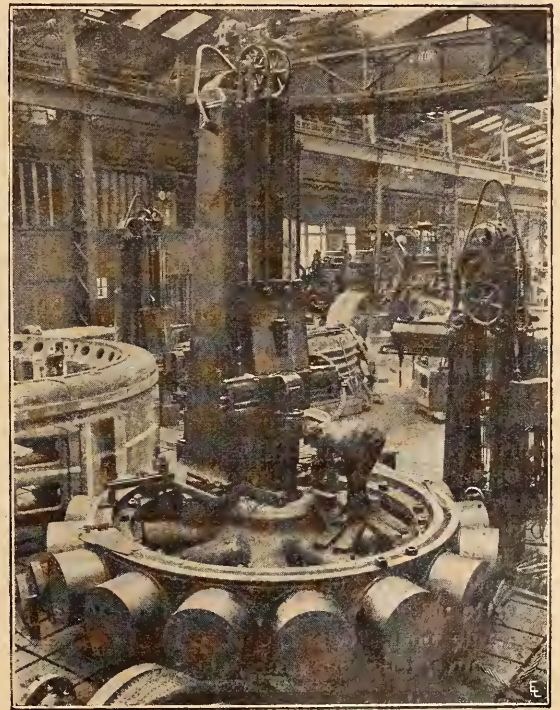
Usinage du rotor d'un alternateur A. S. E. A.
